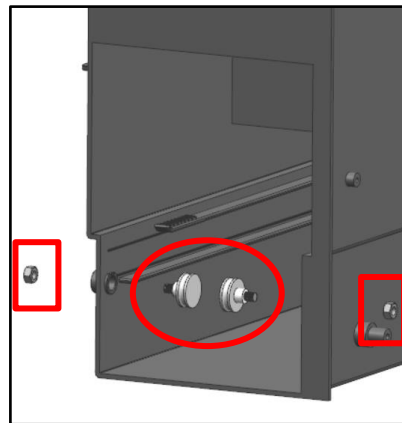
Pompanın buz makinası şasisine montajı.
